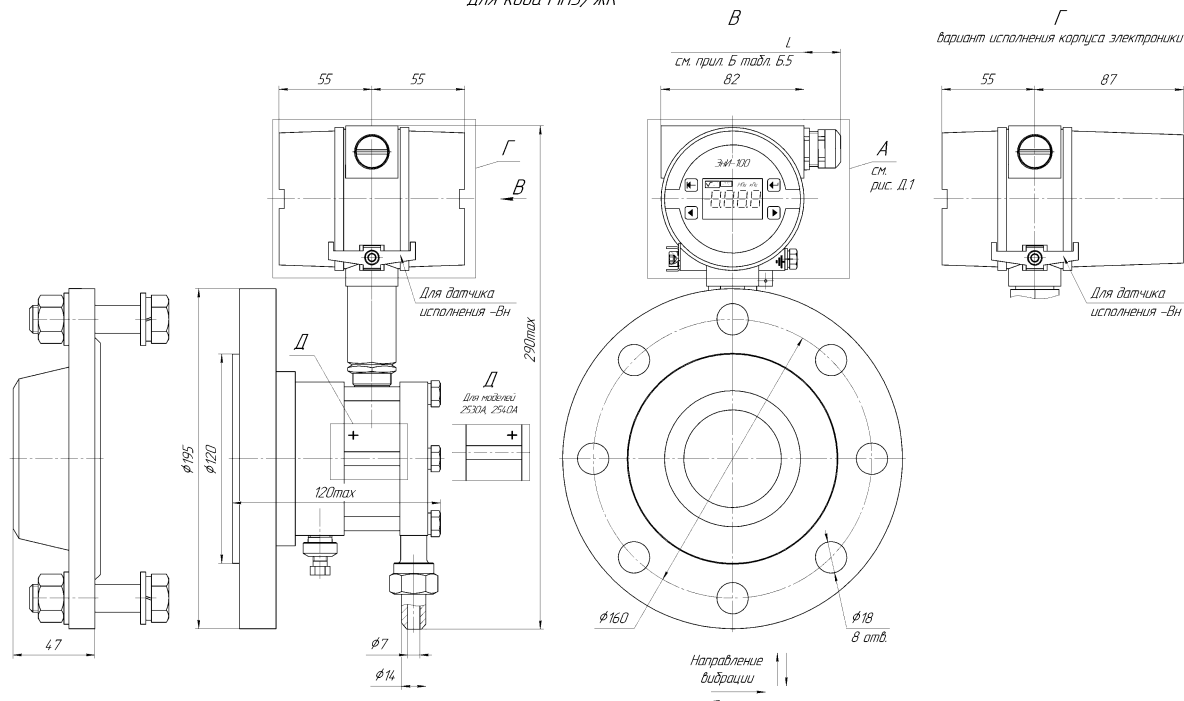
Датчики специального фланцевого конструктивного исполнения моделей 2530, 2540, 2530А, 2540А. Соединение и развальцовка трубопровода $\varnothing 7$ по ГОСТ 13954-74. Фланец присоединительный для установки датчика на стенке резервуара по ГОСТ 12815-80 исп. 3 (ряд 1), PN = 4,0 МПа, DN = 80 мм. В комплекте с фланцем паронитовая прокладка Б-80-100 ПОН по ГОСТ 15180-86
